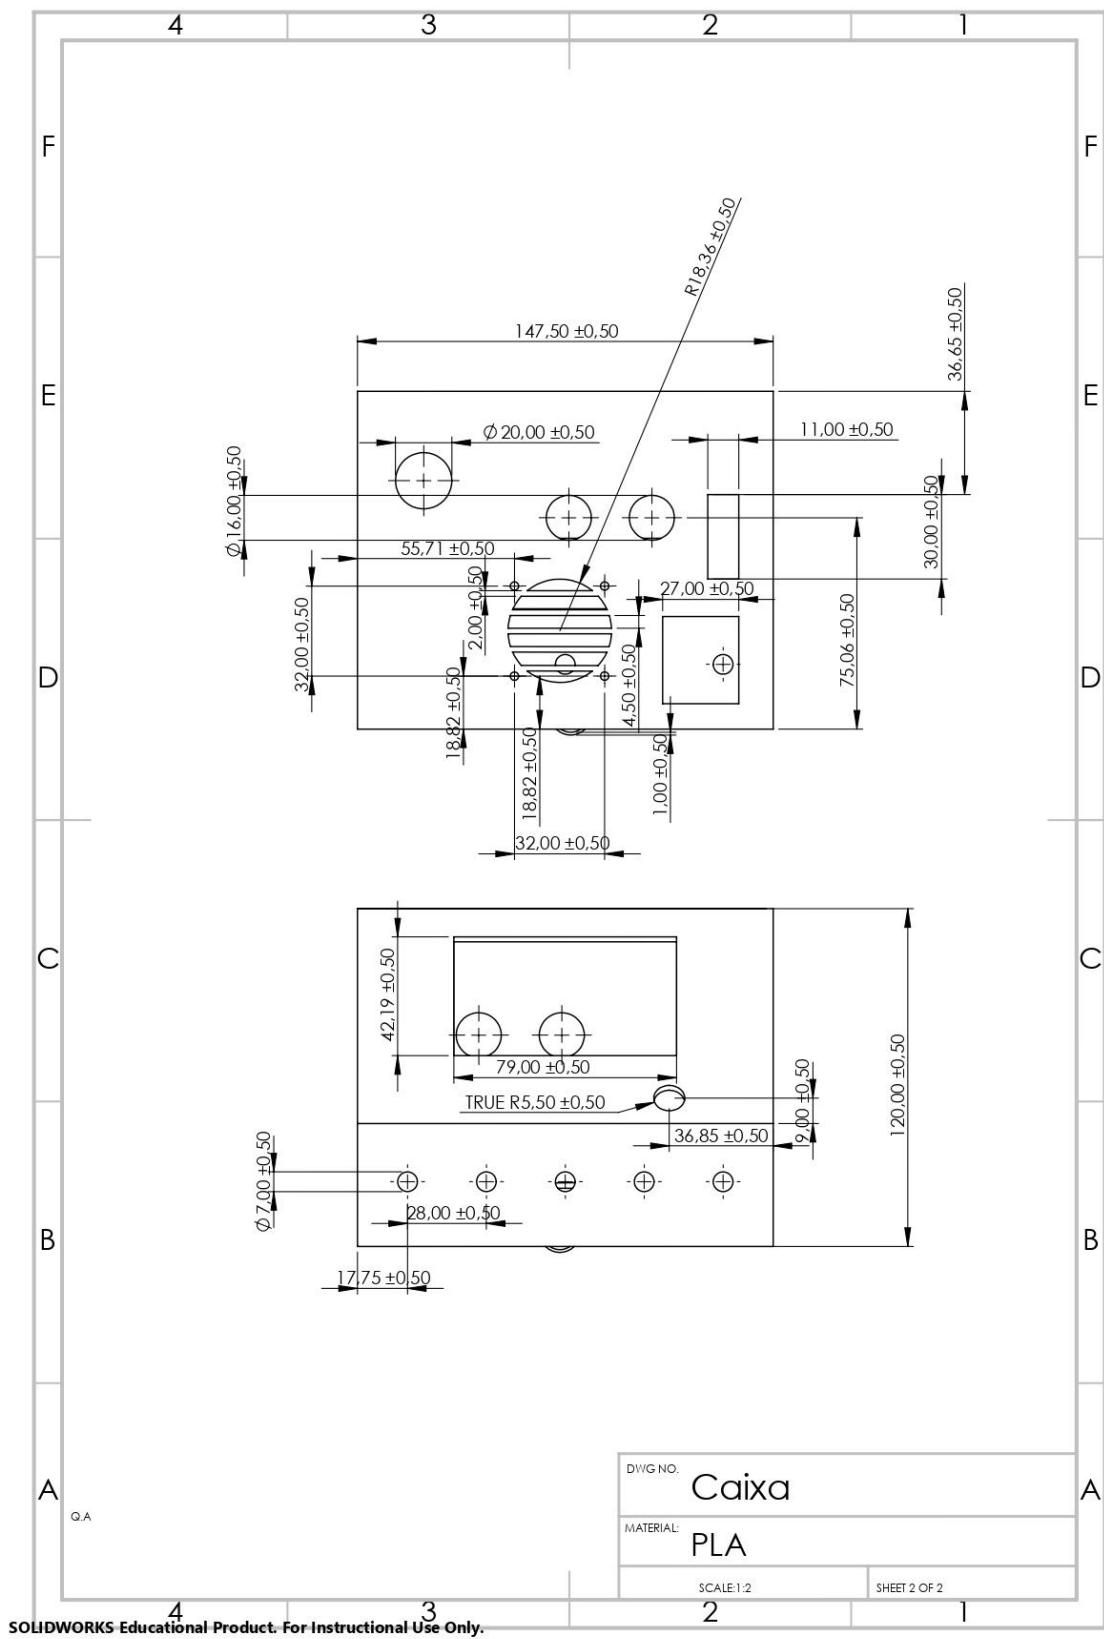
Desenho técnico caixa, vista posterior e frontal.
